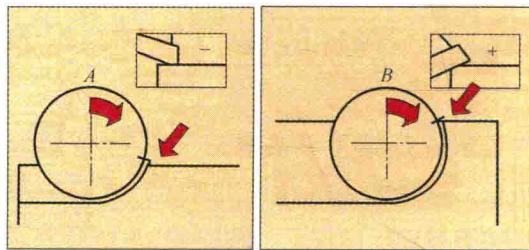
铣刀切削刃与工件间顺利的初始接触方式
